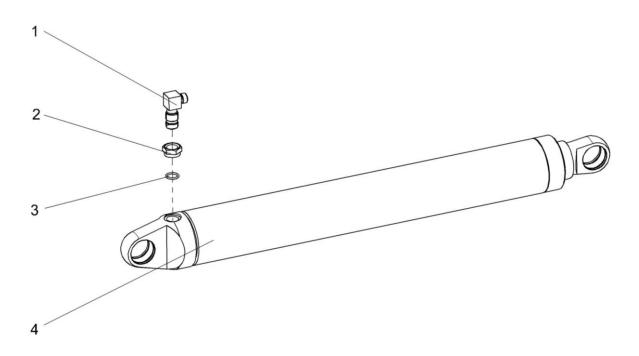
Гидроцилиндр КЗК-10-1-0602500
